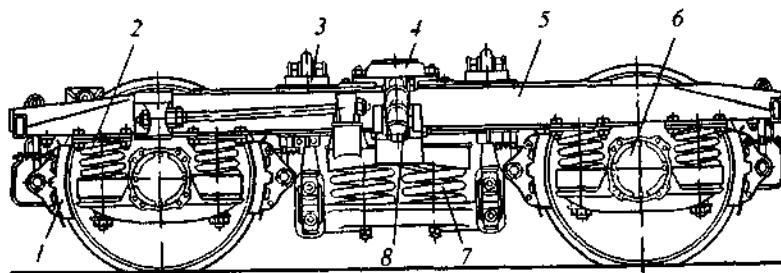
Тележка КВЗ-ЦНИИ пассажирского вагона: 1 — тормозная колодка тележки; 2 — рессорное подвешивание буксовоое; 3 — скользун; 4 — подпятник; 5 — рама; 6 — букса; 7 — рессорное подвешивание центральное; 8 — гаситель колебаний
